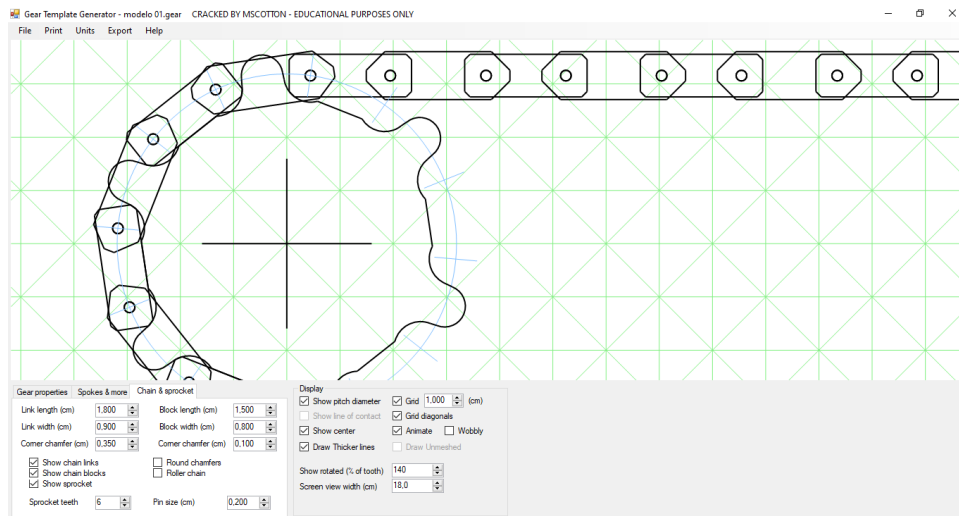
Sistema de engranajes, bloques y uniones diseñado en GearGenerator3.
